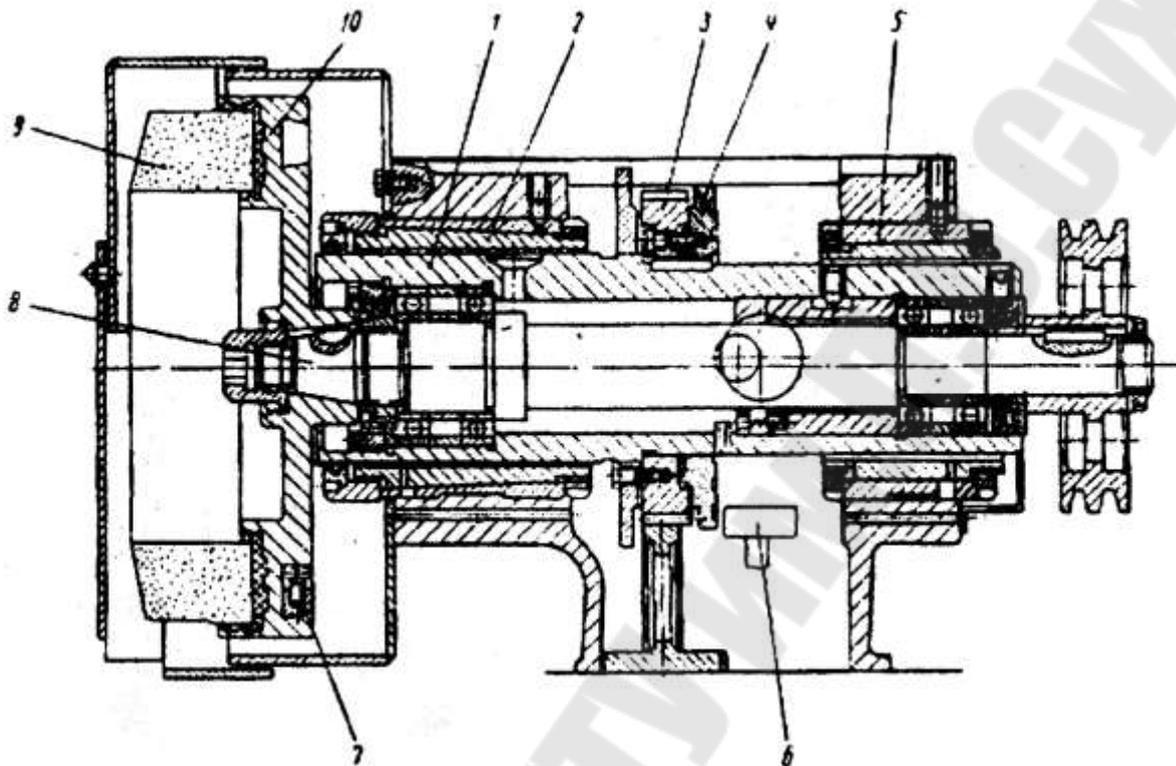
Шлифовальный шпиндель полуавтомата 3659М:
